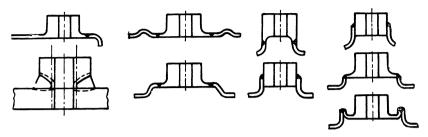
Сварные детали алюминиевых сварных конструкций
